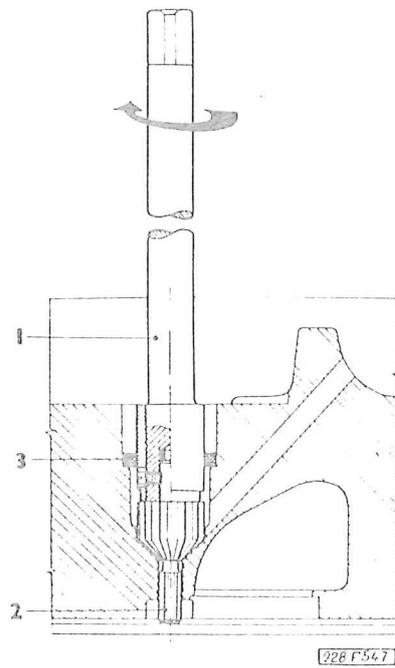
Bearbeitung der Sitzfläche für das Einspritzventil
